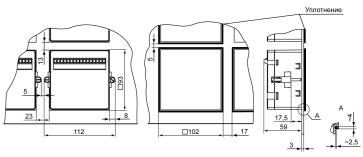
Прибор в корпусе Щ1, установленный в щит толщиной 3 мм
